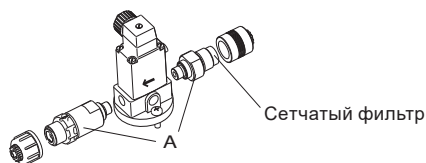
ЭМК OCD-162-30, -60: Сборочный чертёж
